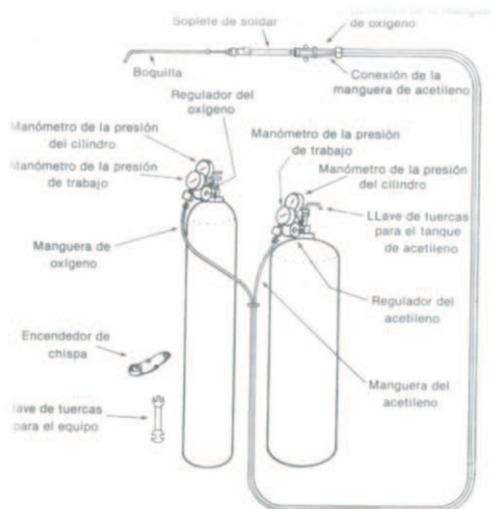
Equipo completo para soldadura oxiacetilénica. (Ilustración redibujada con autorización de Airco Welding Products, División de Airco, Inc., *Oxygen Welding and Oxygen Cutting Instruction Course*, 1966, p. 76.)
